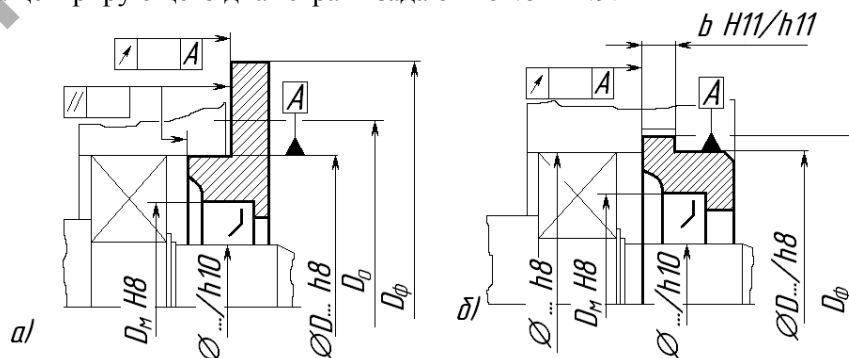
Торцовая и закладная крышки с отверстием для прохода вала
